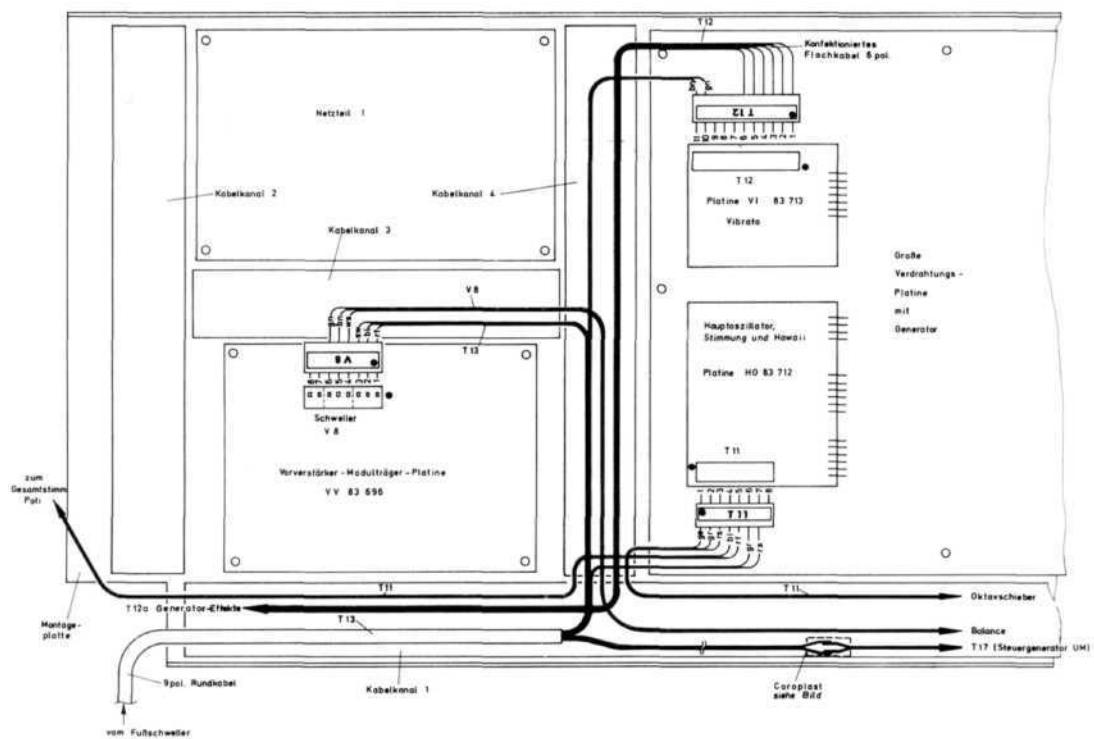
Kabelverlegeplan T 11, T 12, T 13 und V 8
